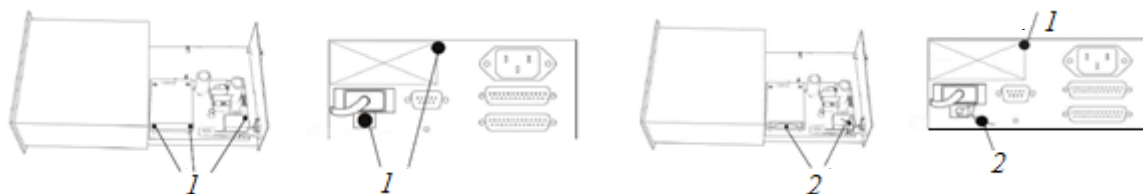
Схема пломбировки корпуса приборов весоизмерительных:
